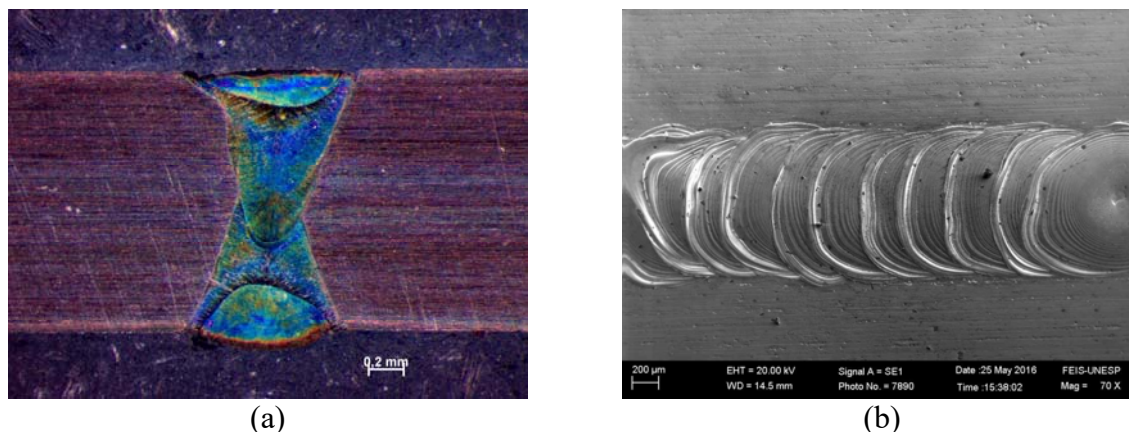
Junta soldada. (a) Corte transversal; (b) Vista Superior.
